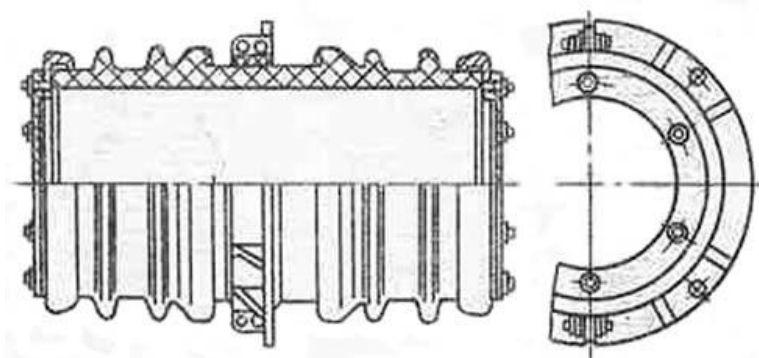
Проходной изолятор для внутренней установки 20 кВ, 8000-12500 А
